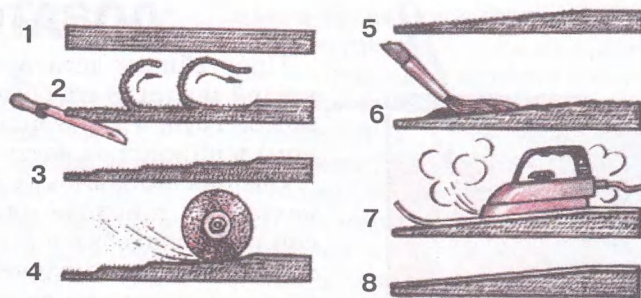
Этапы изготовления ластва из транспортной ленты: 1 — заготовка (транспортная лента); 2 — послойная подрезка; 3 — промежуточная форма; 4 — снятие ступеней абразивным кругом; 5 — подготовленная форма; 6 — покрытие сырой резиной; 7 — вулканизация слоя; 8 — готовый ласт.
